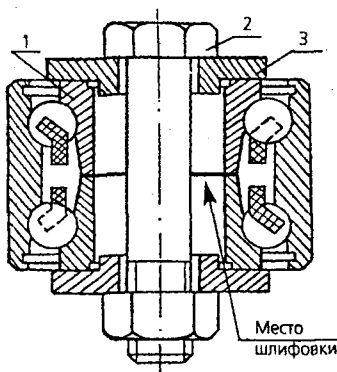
Сборка подшипника стяжкой после шлифовки для проверки на люфт: 1 – кольцо внутренней обоймы; 2 – стяжной болт с гайкой; 3 – шайба
